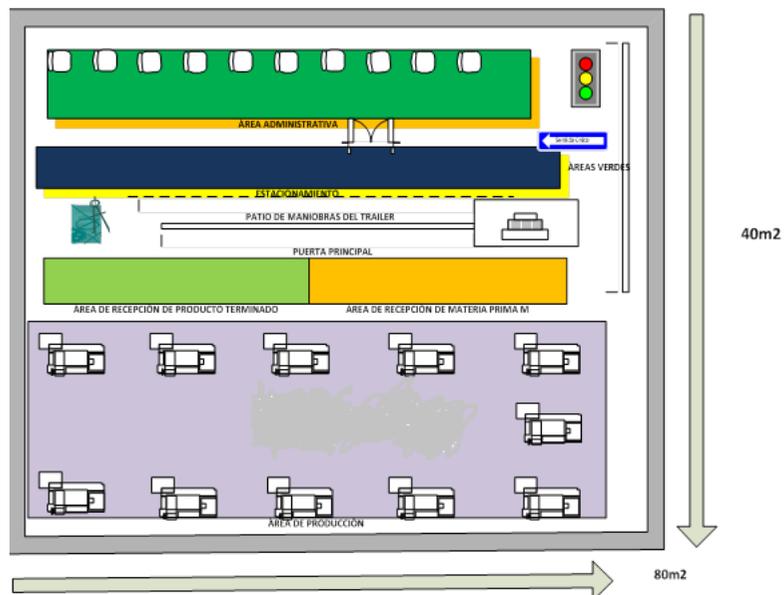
FIGURA IV. XIV PLANTA CON 11 MÁQUINAS
